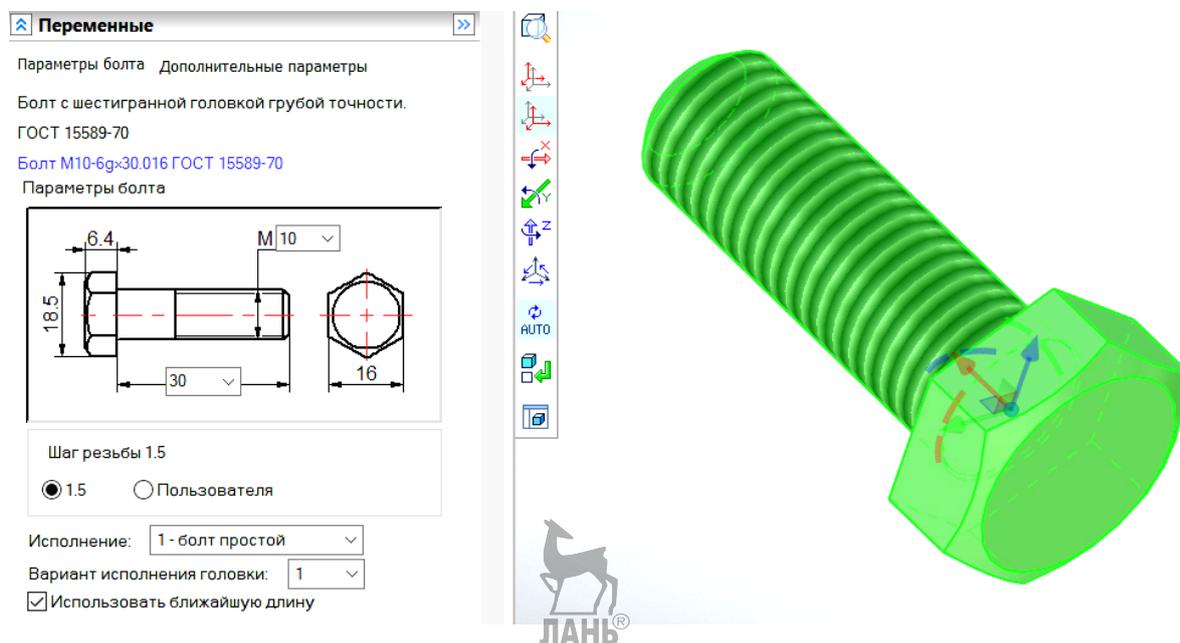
Параметры болта для крепления корпусов шток-реек
